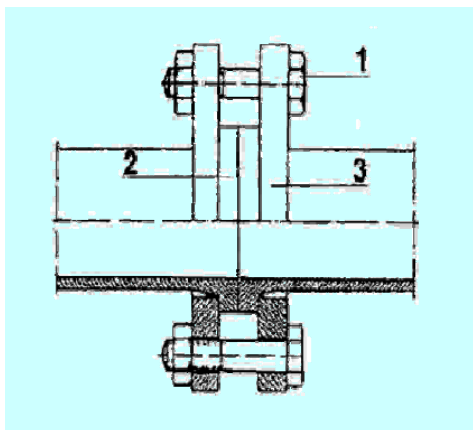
Structura îmbinării prin ștuț cu guler și flanșă
